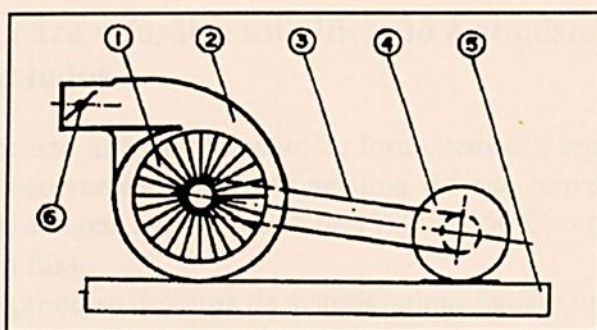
Insuflador de ar: 1 - rotor; 2 - carcaça; 3 - correia; 4 - motor; 5 - suporte de madeira, e 6 - válvula reguladora do fluxo de ar.
